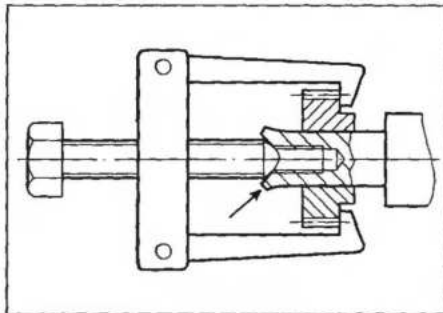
Пример некачественной разборки - развальцовка хвостовика коленчатого вала болтом съемника до полной невозможности спрессовать шестерню
